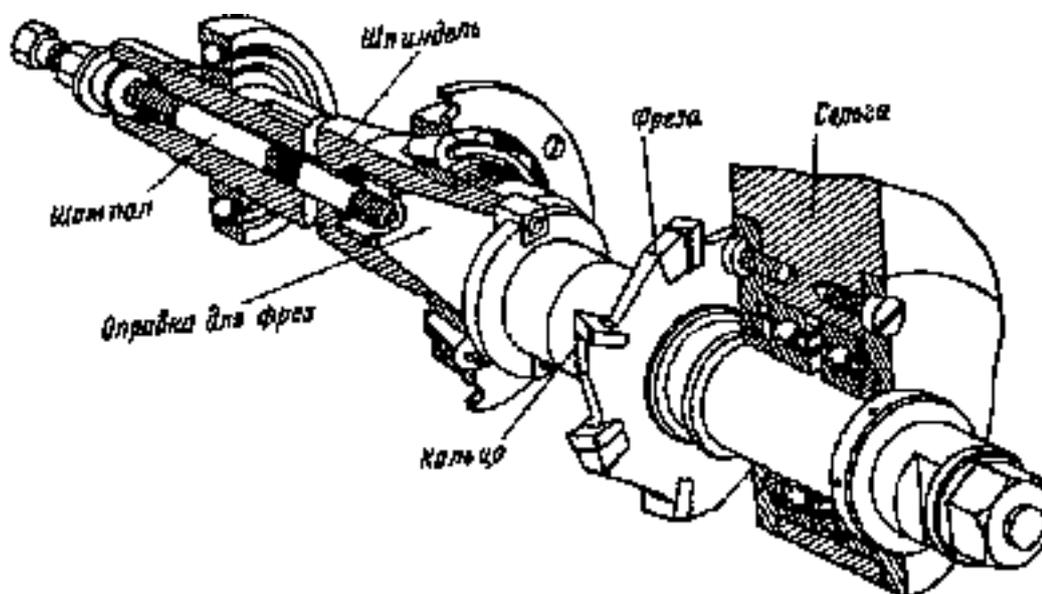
Установка инструмента на консольно-фрезерных станках 6Н81Г
